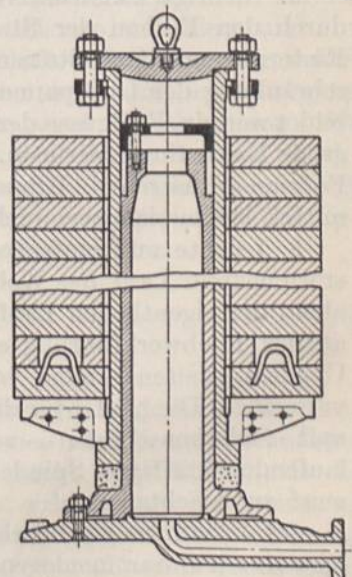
Druckwasserspeicher. Der Zylinder bewegt sich auf einem ruhenden Kolben.
